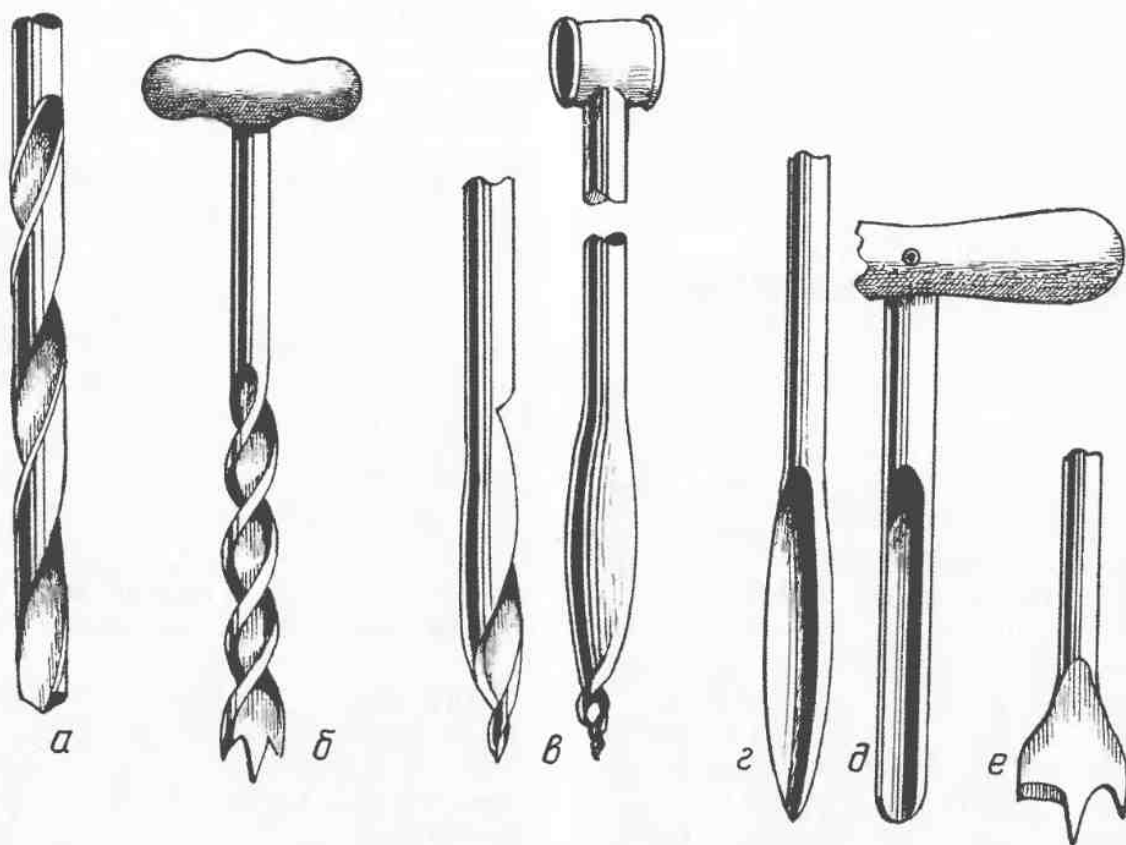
Сверла для сверления древесины: а — спиральное сверло; б — бурав обыкновенный; в — бурав ложечный; г — ложечное сверло; д — самодельное сверло из трубки; е — перьевое сверло (центровая перка)
